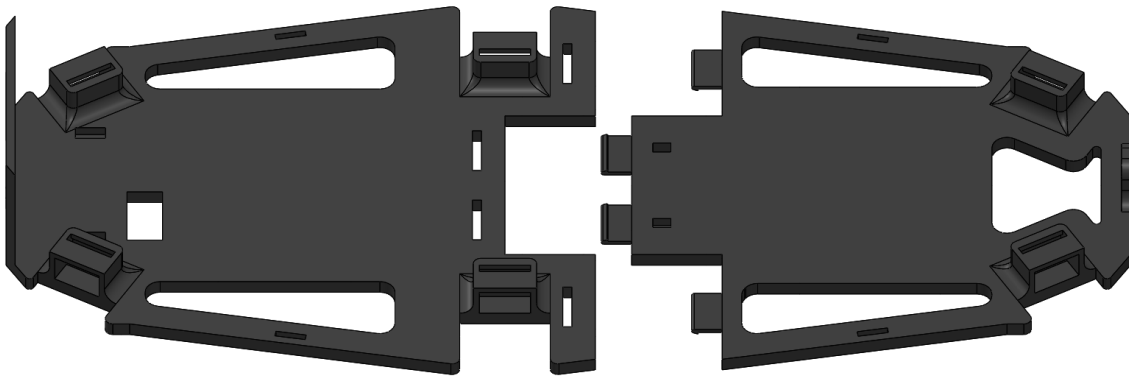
Vista explosionada de la parte del chasis superior. A la derecha chasis superior trasero, a la izquierda el delantero.
